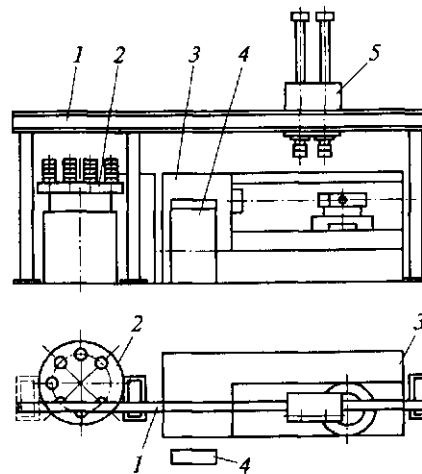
Схема РТК с порталным роботом для токарной обработки: 1 — ПР; 2 — дисковый магазин (поворотный стол); 3 — токарно-револьверный станок с ЧПУ; 4 — устройство управления ПР; 5 — манипулятор
